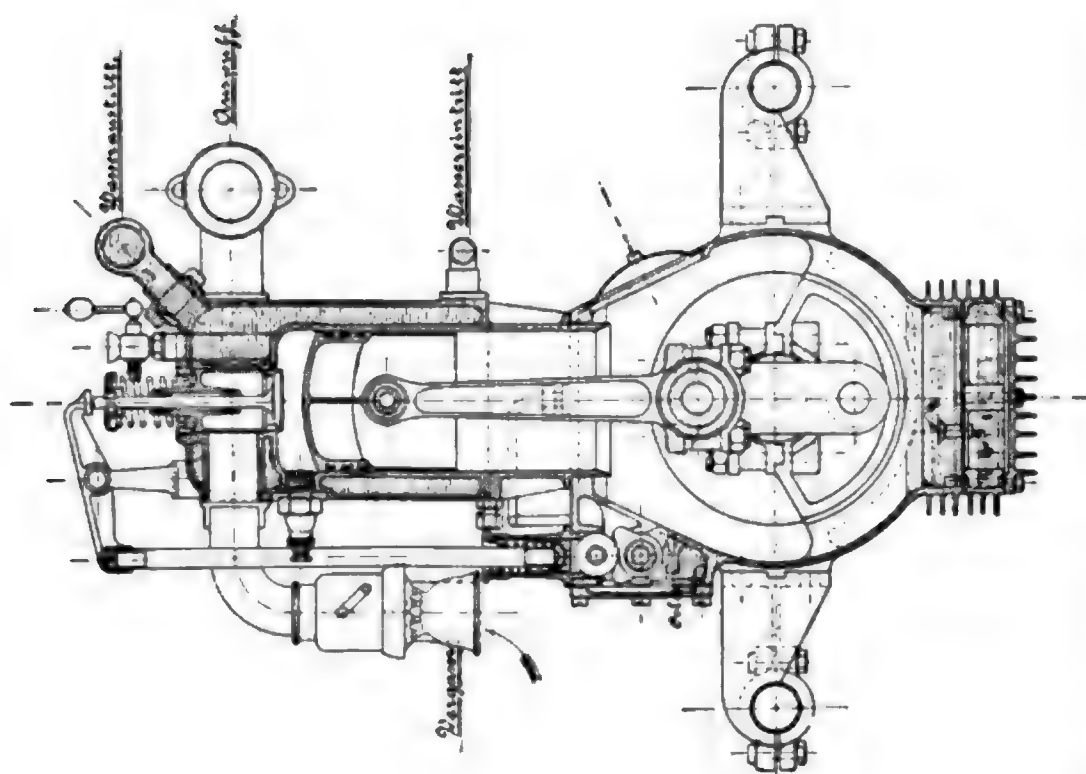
Zeichnung des Flugmotors von Escher & Co., Querschnitt.
